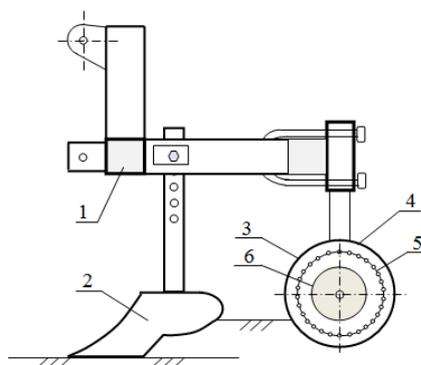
Схема окучника и прикатывающего катка для измельчения поверхностной корки грядок:
